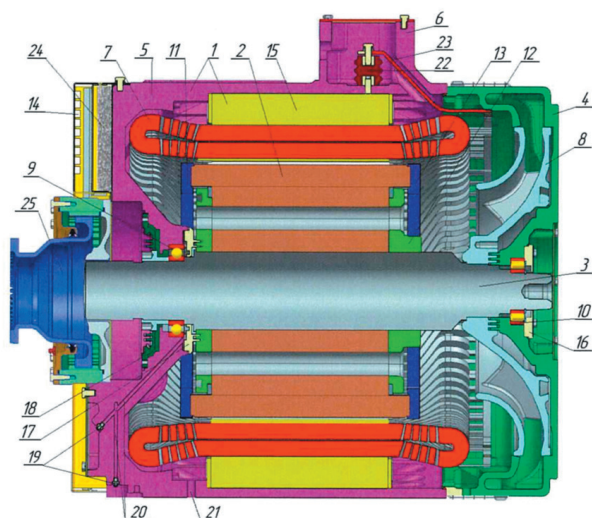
Расположение основных элементов тягового электродвигателя: 1 — статор; 2 — ротор; 3 — вал ротора; 4 — подшипниковый щит; 5 — станина; 6 — коробка выводов; 7 — обмотка статора; 8 — вентилятор; 9 — шарикоподшипник; 10 — роликовый подшипник; 12 — упорная шайба; 11, 13 — короткозамыкающие кольца; 14 — воздухозаборная решетка; 15 — сердечник статора; 16 — крышка подшипника (сторона НП); 17 — крышка подшипника (внутренняя); 18 — крышка подшипника (наружная); 19 — масленка; 20 — масляный канал; 21 — отверстие для слива конденсата; 22 — изолятор; 23 — фазная шина; 24 — фильтровальное полотно; 25 — полумуфта
